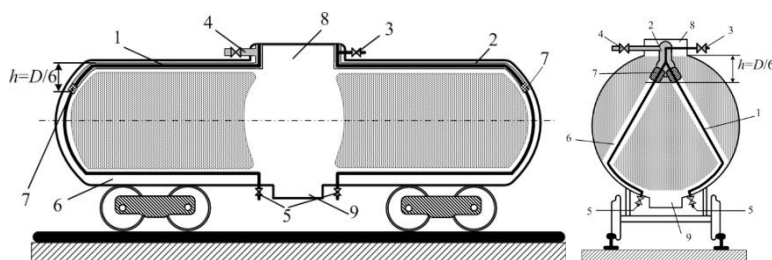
Устройство двухэтапного размыва застывшей фракции ЗНГ:
